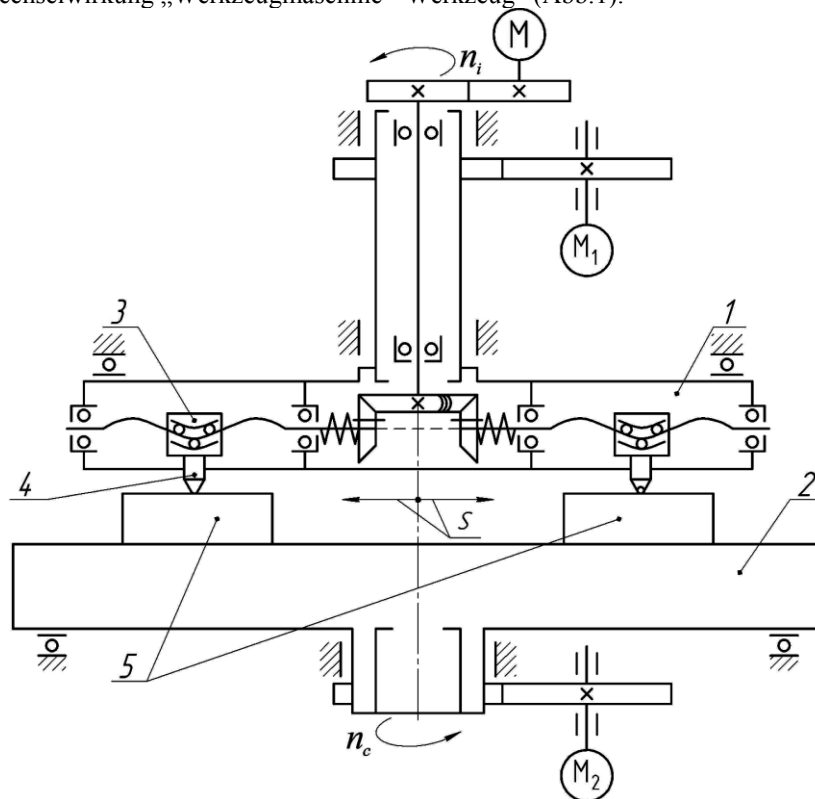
Die Variante der formgebenden Bewegungen bei der Wechselwirkung „Werkzeugmaschine - Werkzeug“
